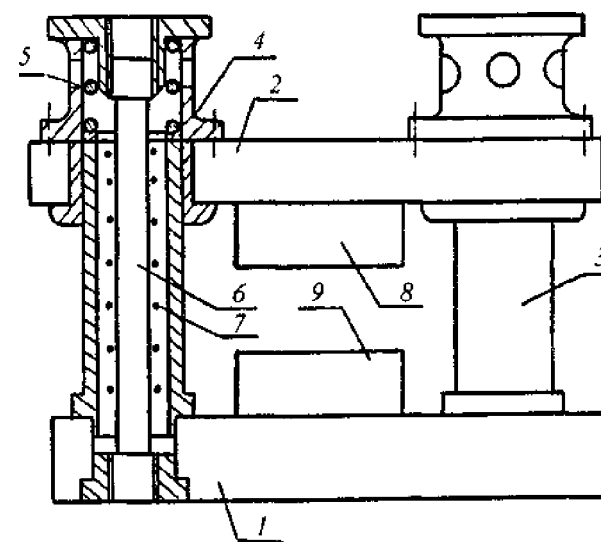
Принципиальная схема пресс-штампа: 1 - нижняя плита; 2 - верхняя плита; 3 - направляющие колонки; 4 - деталь в виде колпачка; 5 - возвратная пружина; 6 - силовой элемент; 7 - электронагреватель; 8 - пуансон; 9 - матрица
